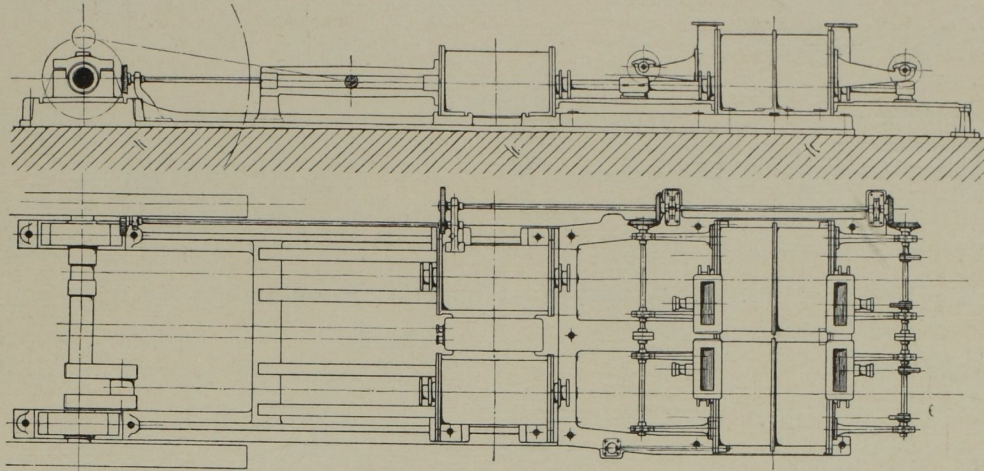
Seitenansicht und Grundriss. Massst. 1:100.
